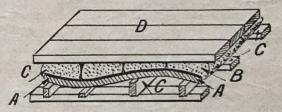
Placage au sable : A, pièce à plaquer; B, sacs de sable ou de son; C, châssis maintenant le dessous; D, planches serrant sur les sacs.
